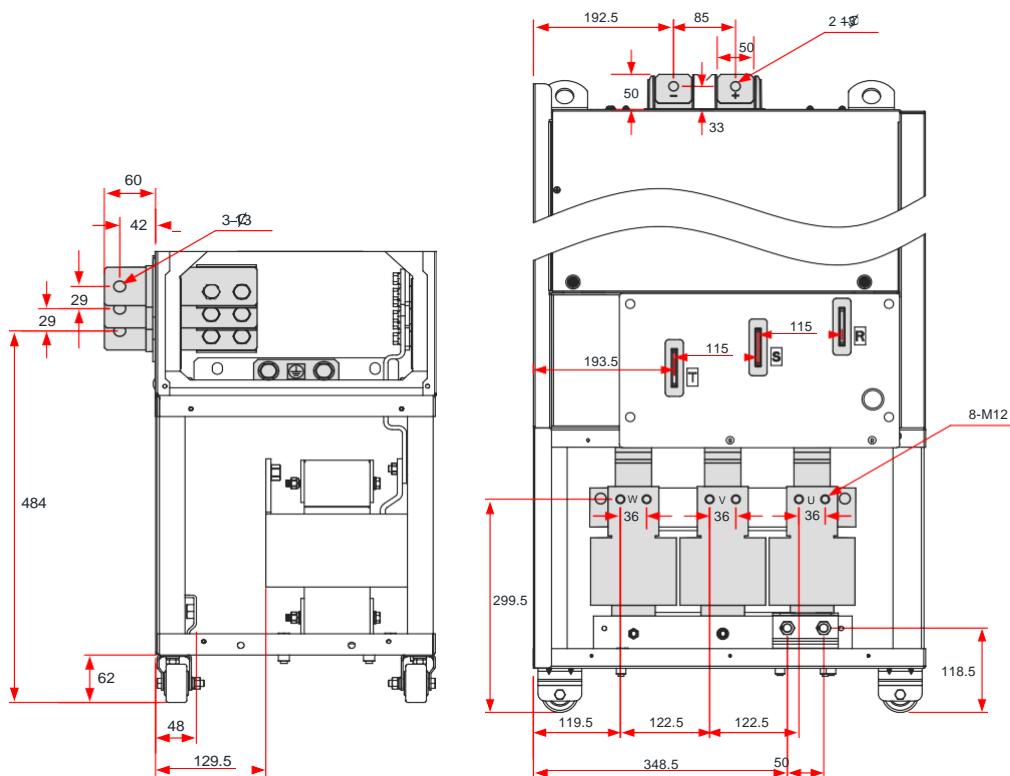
GT600-4T250G-L/ GT600-4T280G-L 主回路端子尺寸 (带输出电抗
